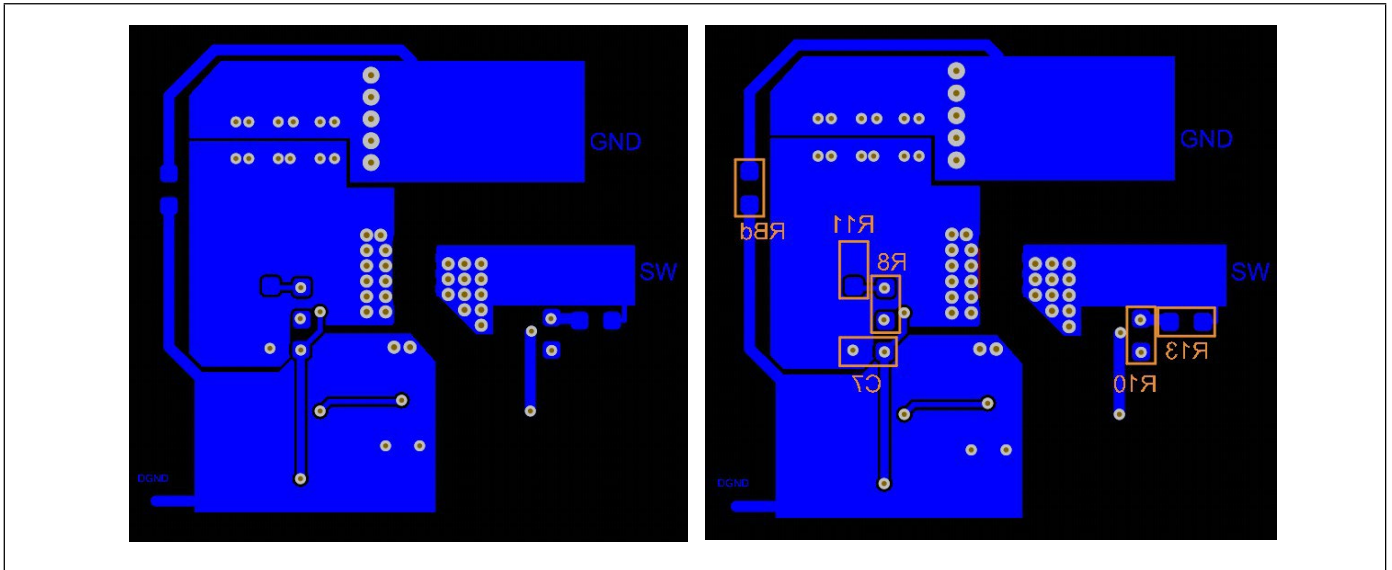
PCB 底层 - 顶视图 (左侧为走线, 右侧为丝印层)
